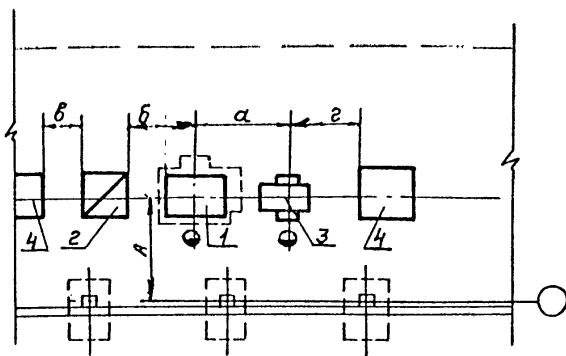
Схема расположения штамповочных линий на базе винтовых прессов с дугостаторным приводом:
